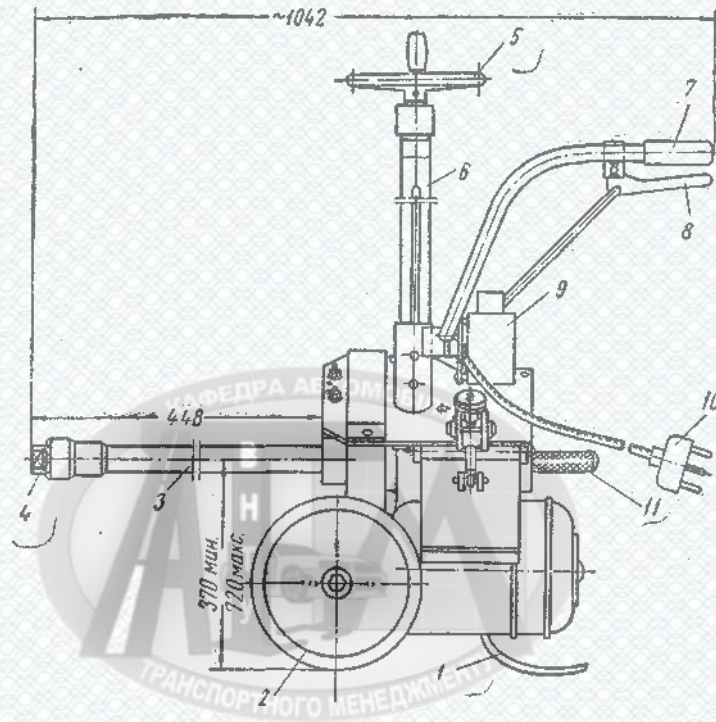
Електромеханічний гайковерт для гайок коліс
